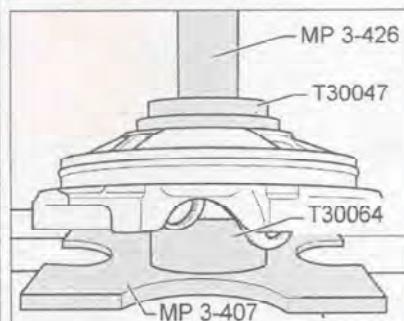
Установка наружной обоймы большого роликоподшипника.
